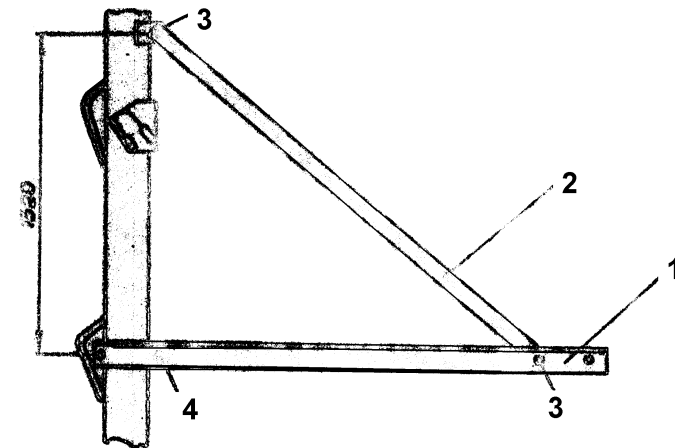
Установка прицепки для борон ПНЛ 13.000
